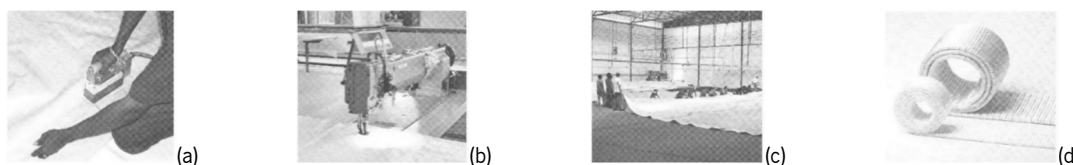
(a) Dispositivo manual de soldadura; (b) máquina de costura industrial; (c) dobragem de uma membrana produzida, pronta para ser transportada; (d) cintas feitas de fibra de poliéster (Knippers et al, 2011).
